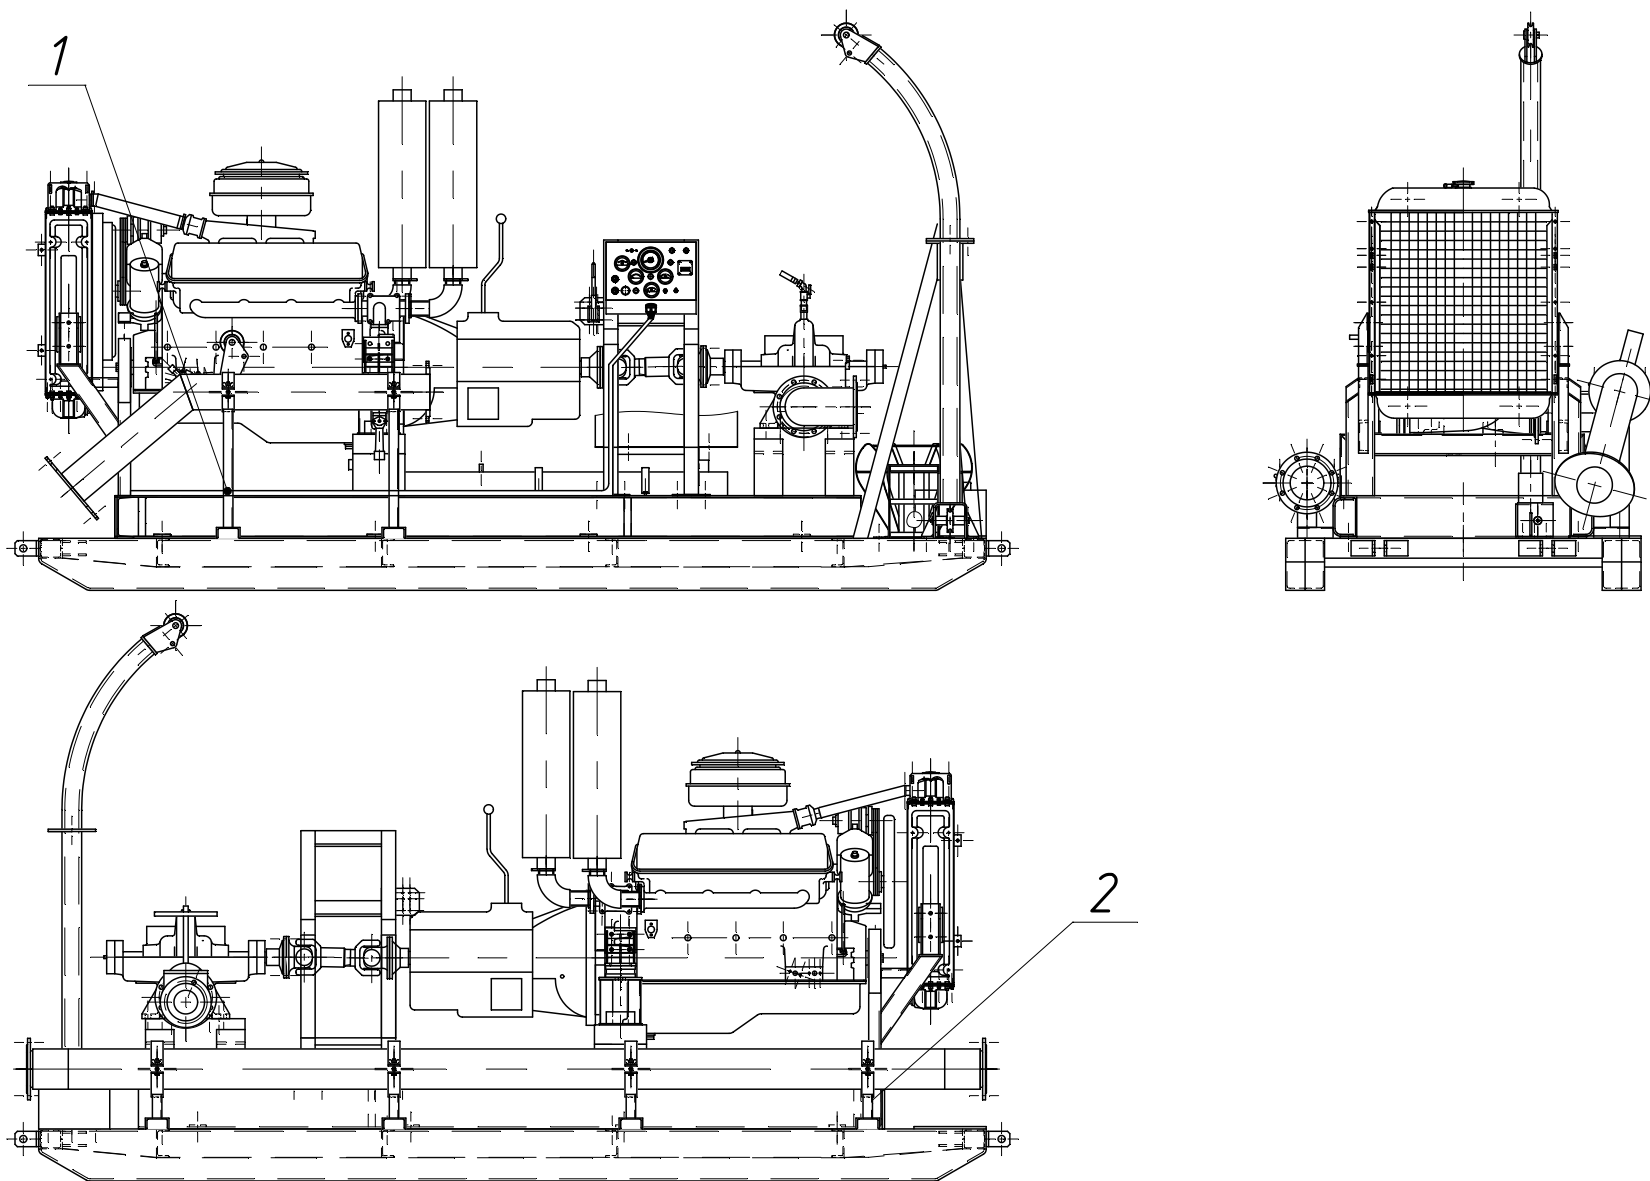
Общий вид агрегатов типа ДНА-П в транспортном положении
